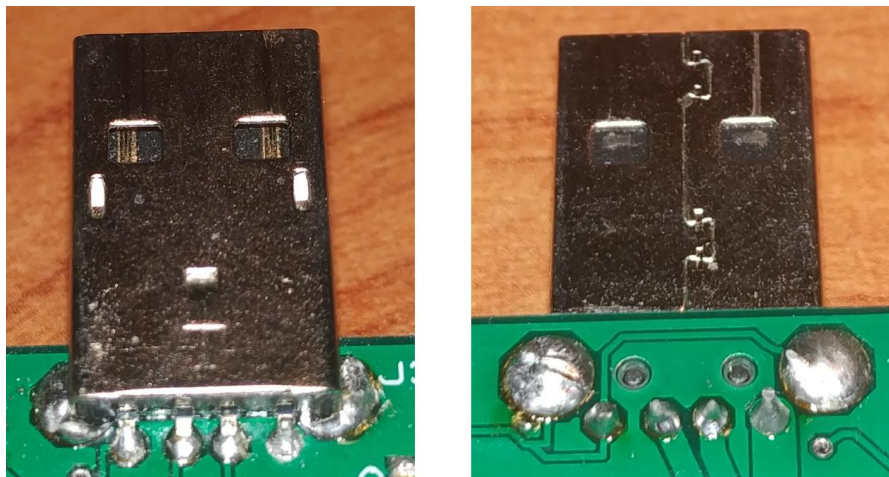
Conector USB tipo A soldado a la PCB
